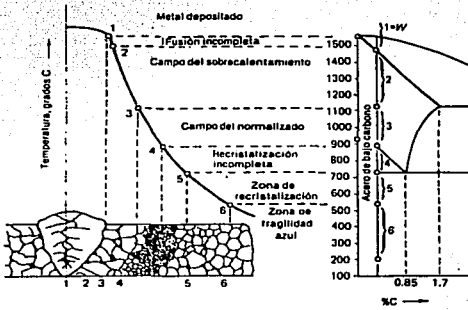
Solidificación Progresiva de la unión soldada.
